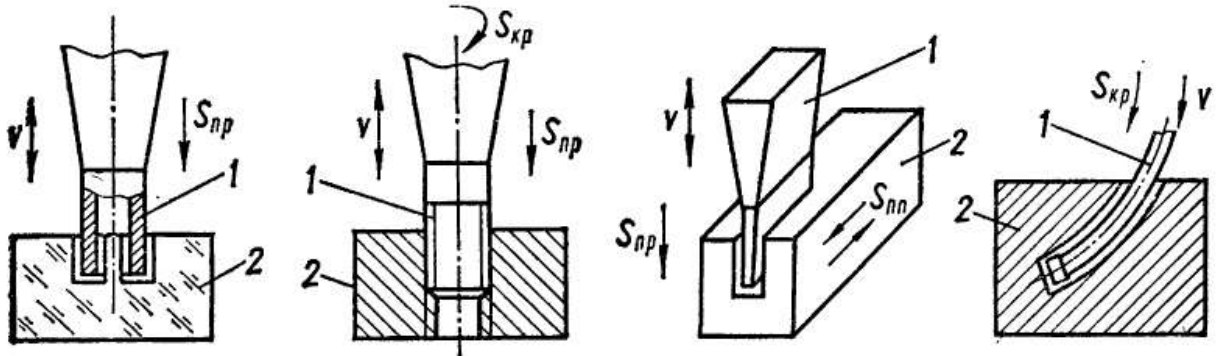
Приклади типової ультразвукової обробки: а – кільцева канавка; б – різьблення; в – паз; г – отвір із криволінійною віссю; V -коливання інструменту під дією ультразвуку (головний рух різання); $S_{кр}$ - кругова подача інструмента; S_{np} - поздовжня подача; S_{nn} – поперечна подача; 1 – інструмент, 2 – заготовка.
